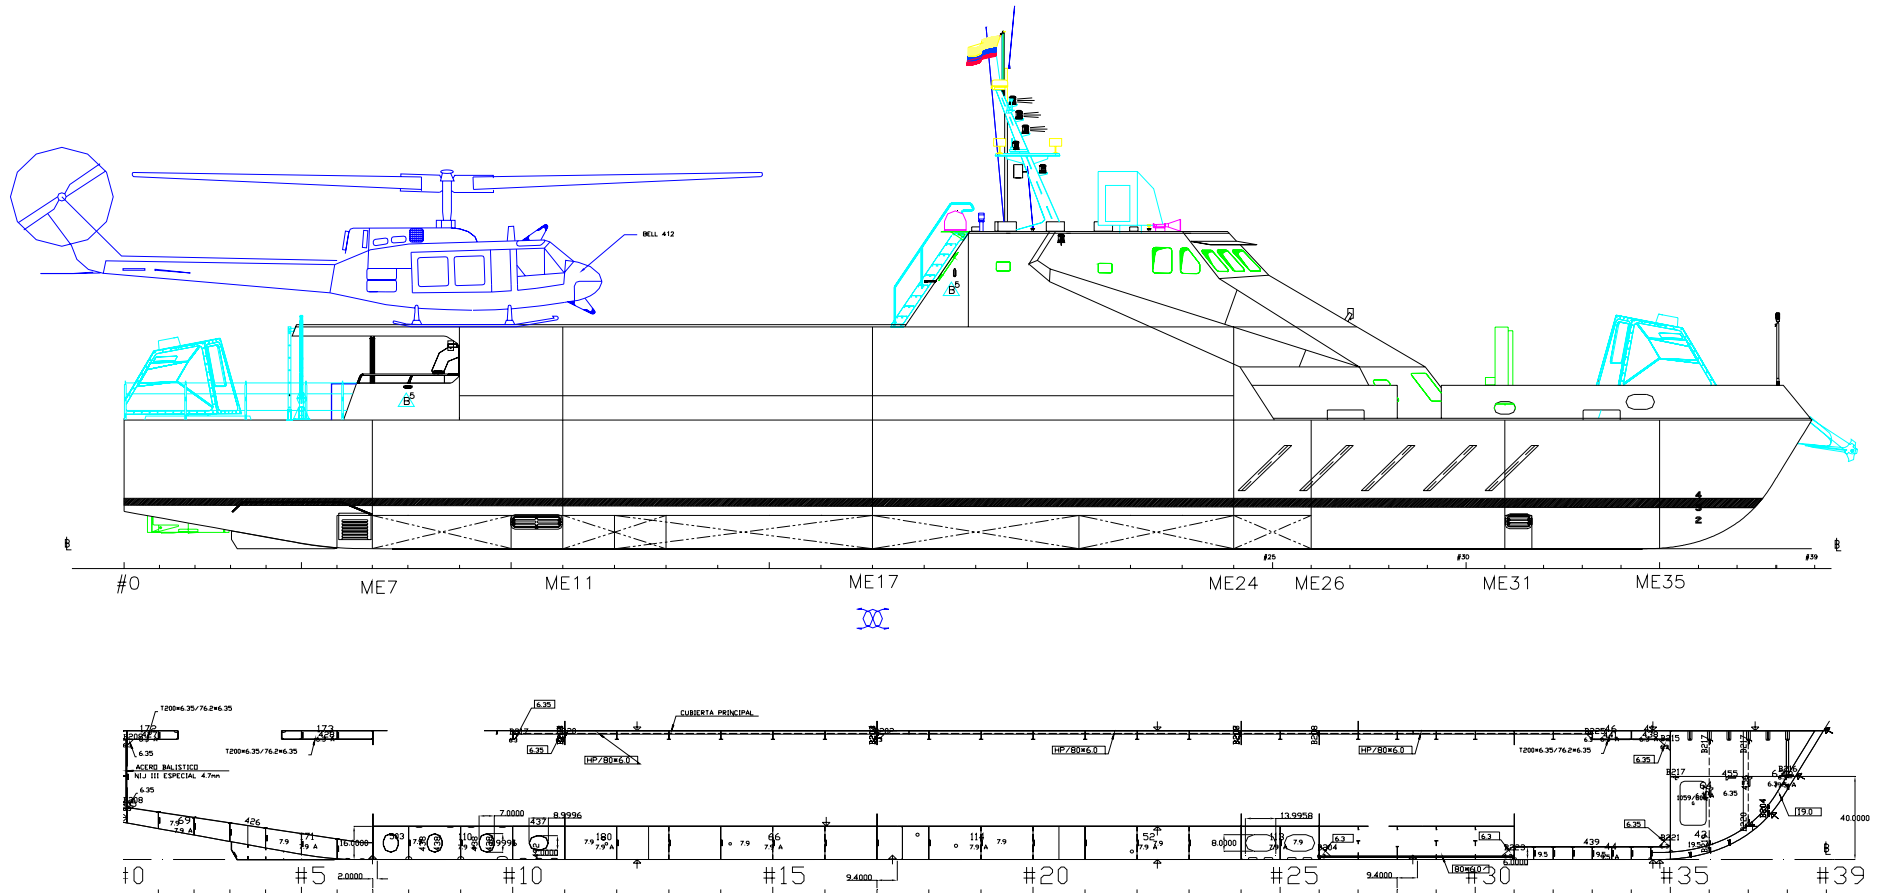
Vista de perfil geral e vista estrutural na linha central
